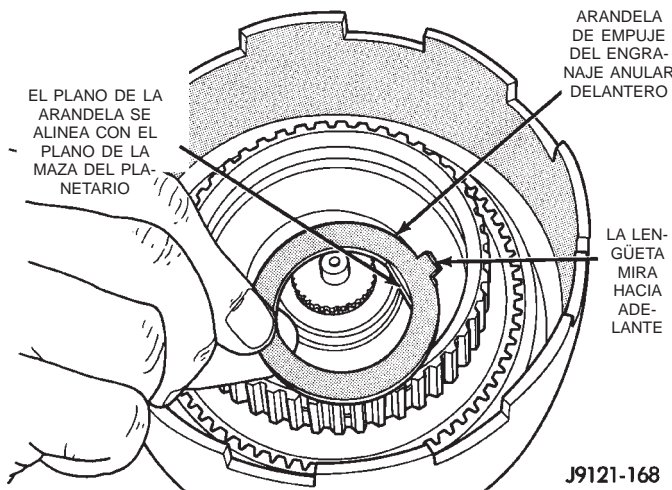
Instalación de la arandela de empuje del engranaje anular delantero
